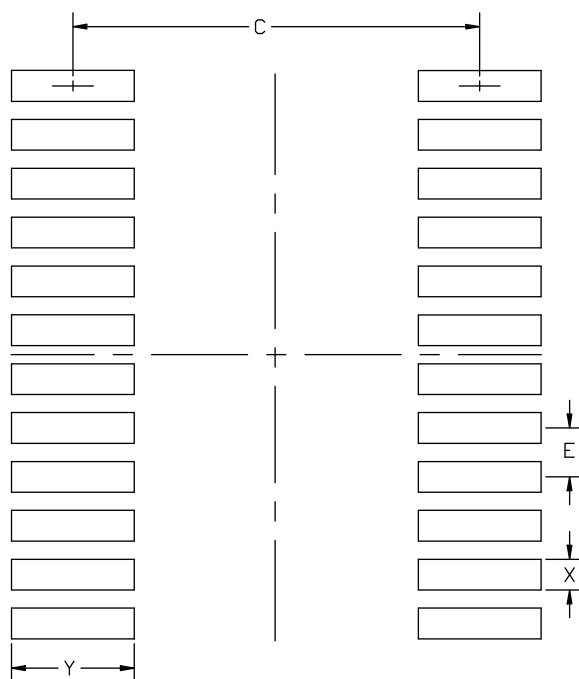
QSOP24 PCB 焊盘布局图
